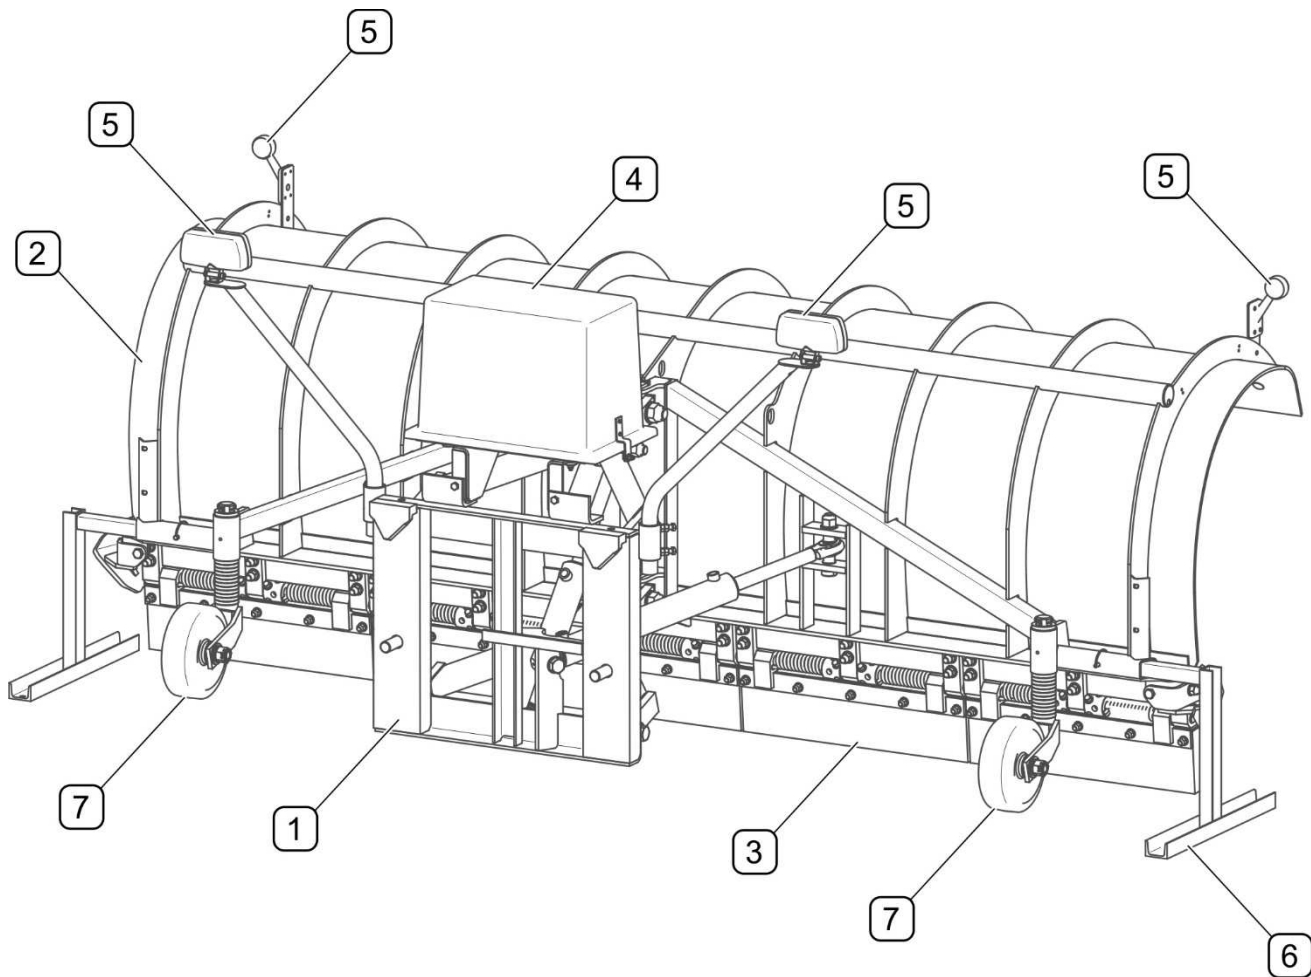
Construction générale (commande électro-hydraulique)
